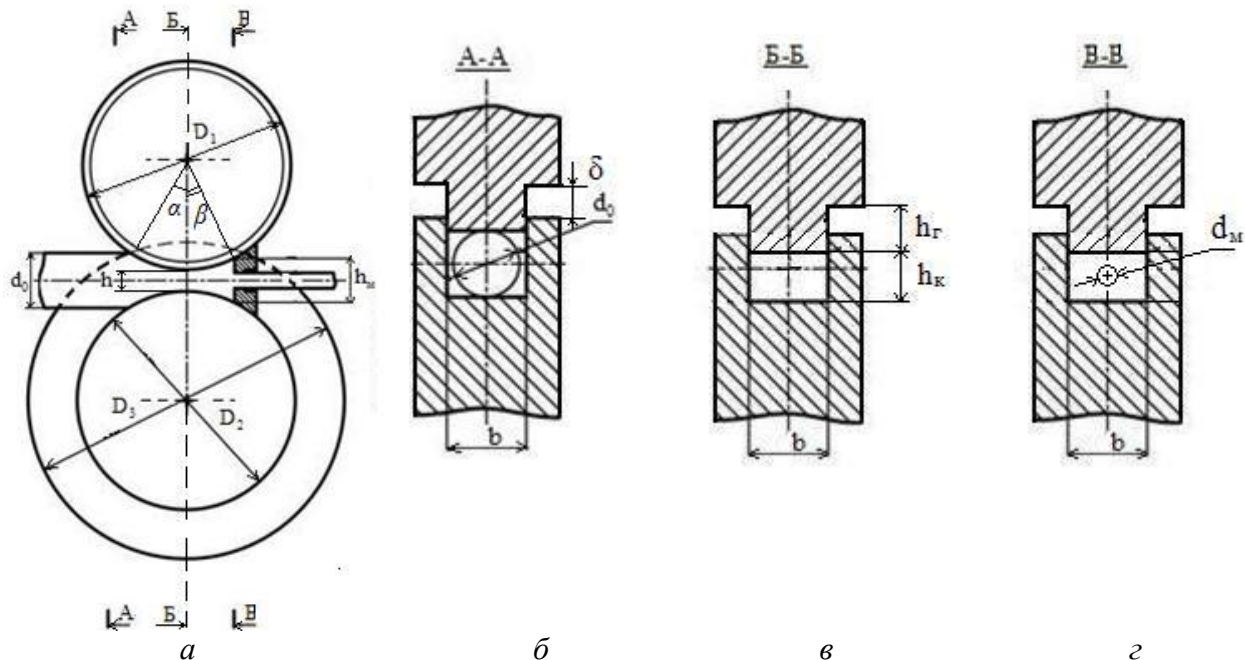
Схема процесса совмещенной прокатки-прессования заготовки круглого сечения в закрытом ящичном калибре: а – общий вид; б – на входе в очаг деформации, в – при прокатке, г – при выдавливании пресс-изделия из матрицы
